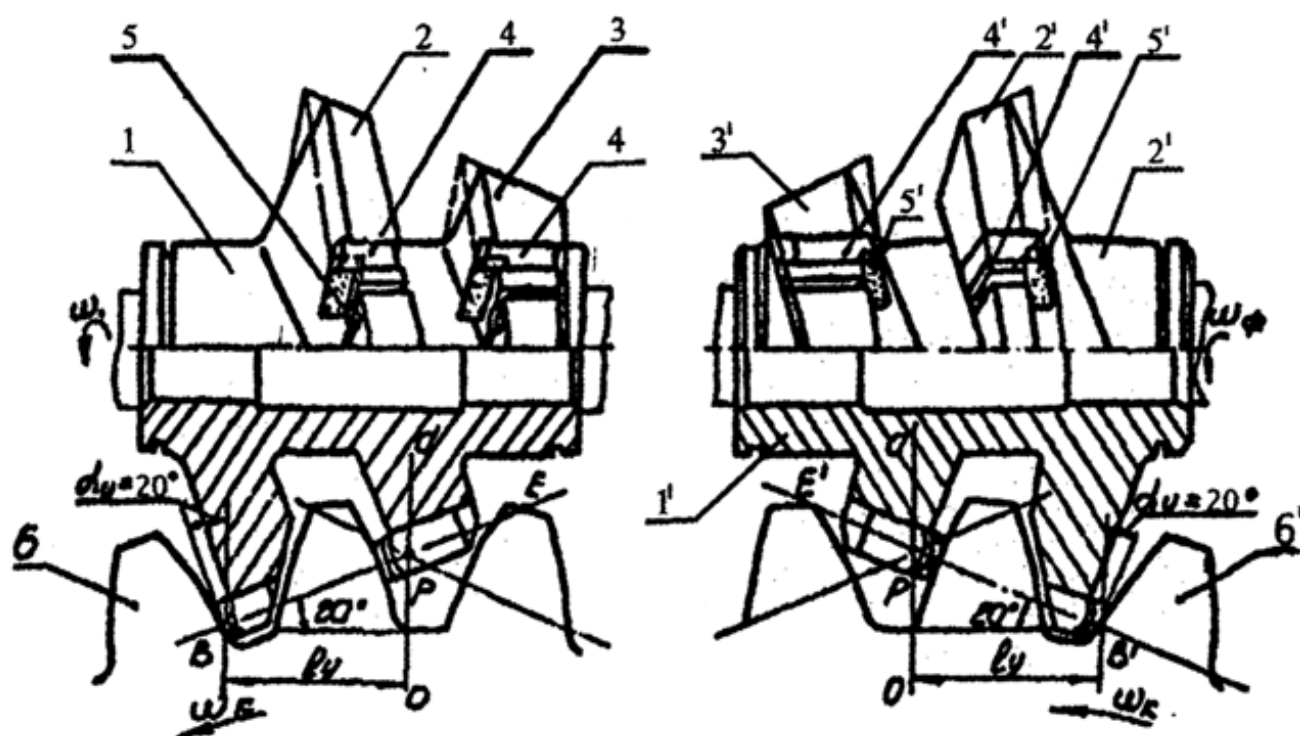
Схема нарезки зубьев двухкорпусной фрезой «Победа».
